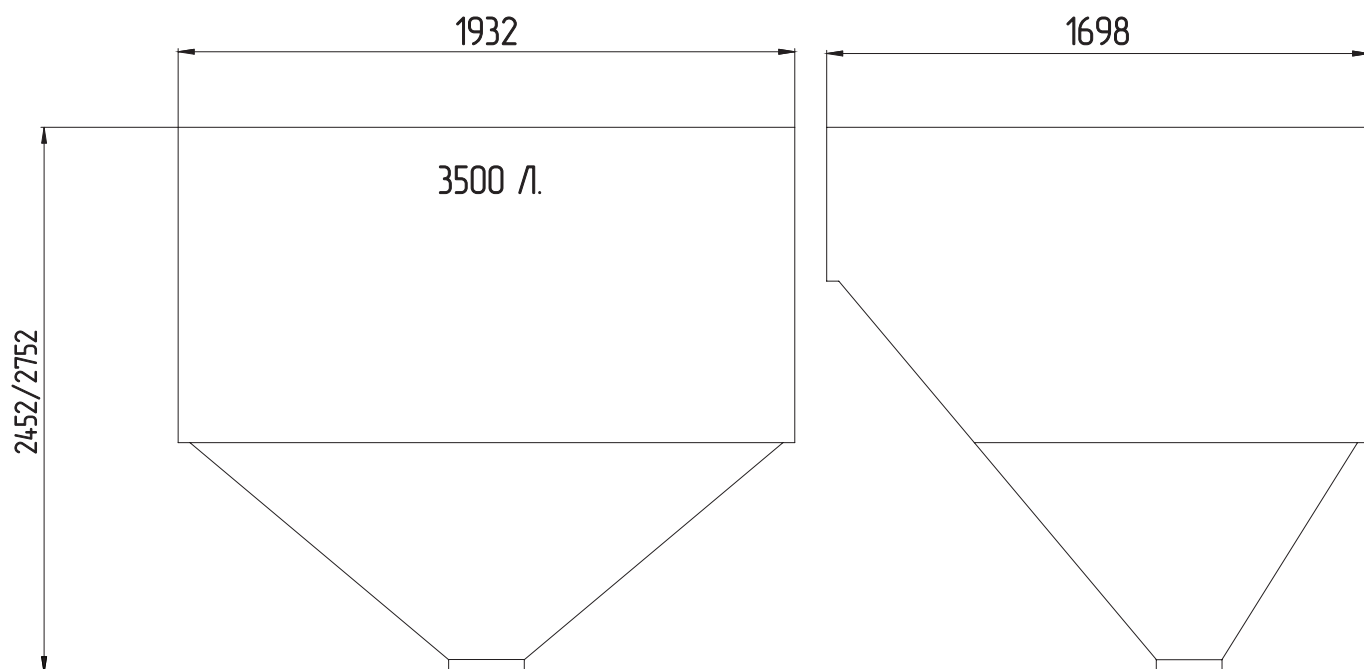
Габаритные размеры топливного бункера 3500 л 1 горло
